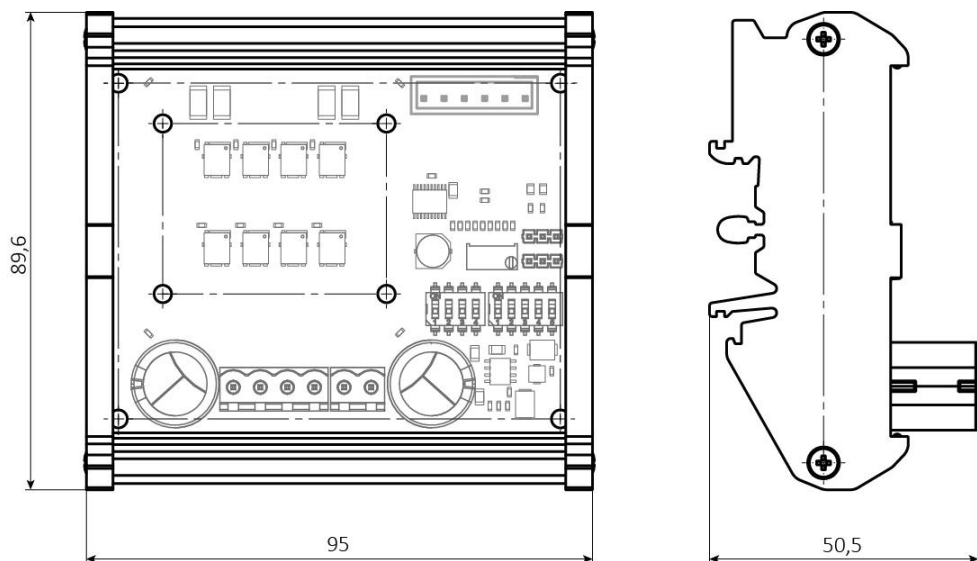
Габаритные и присоединительные размеры драйвера шагового двигателя SMD-4.2 с DIN-фиксатором.
